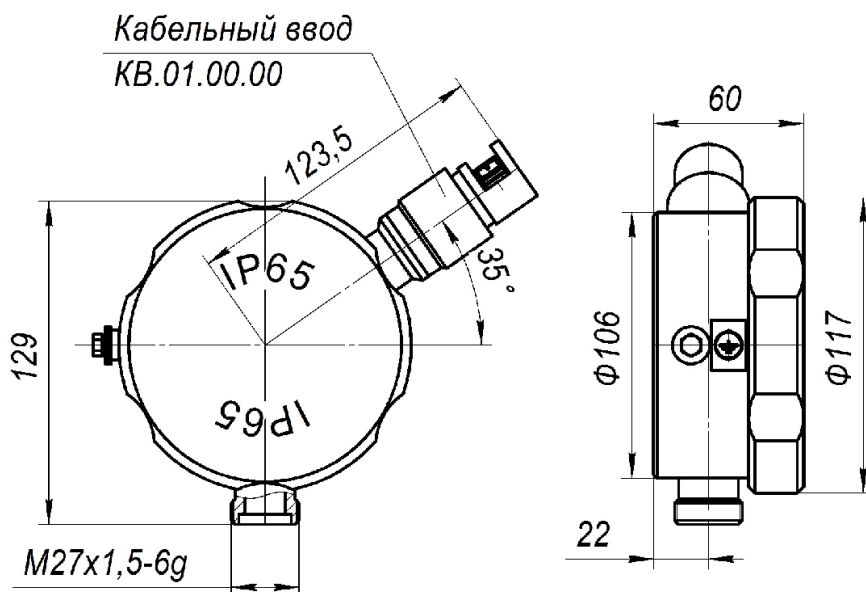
Габаритные, установочные и присоединительные размеры первичного преобразователя АЖК-3122.х.АС, тип "Н" (нерж. сталь)
